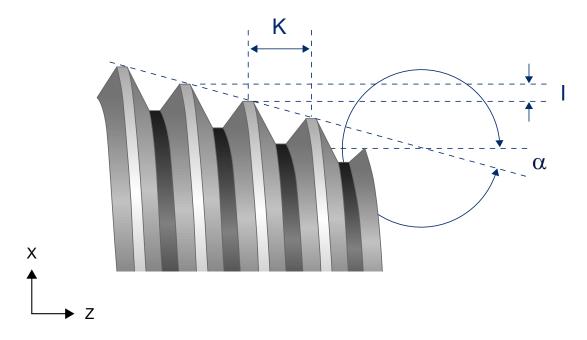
Angabe der Gewindesteigung bei Kegelgewinde
